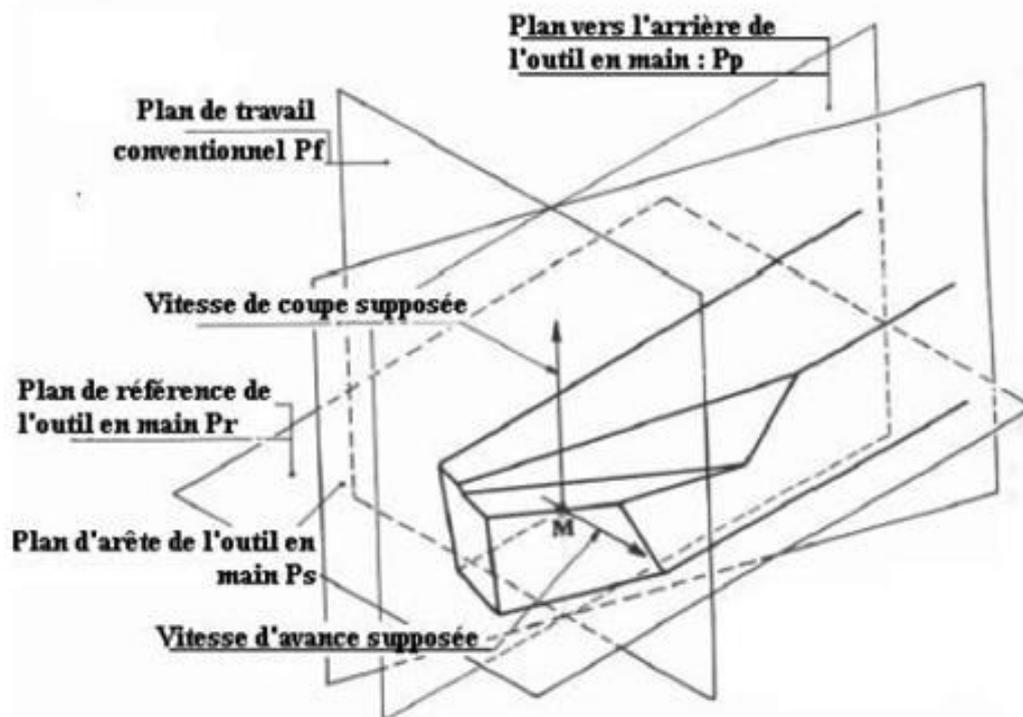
Plans sur un outil en main [Norme NF E 66-502] [18]
